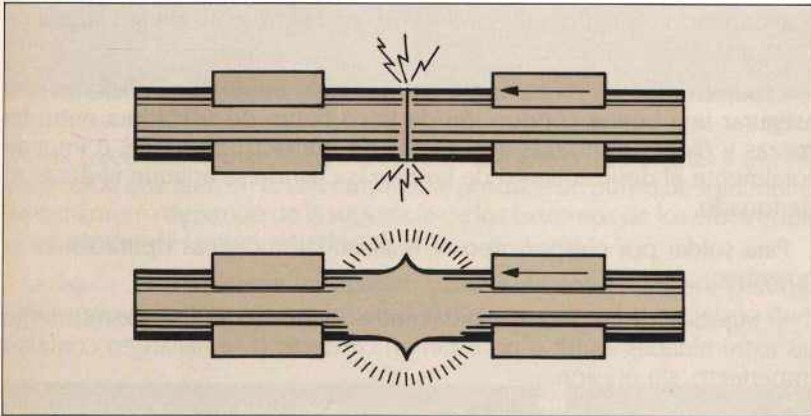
Disposición de los electrodos en soldadura a tope por recalcado.
